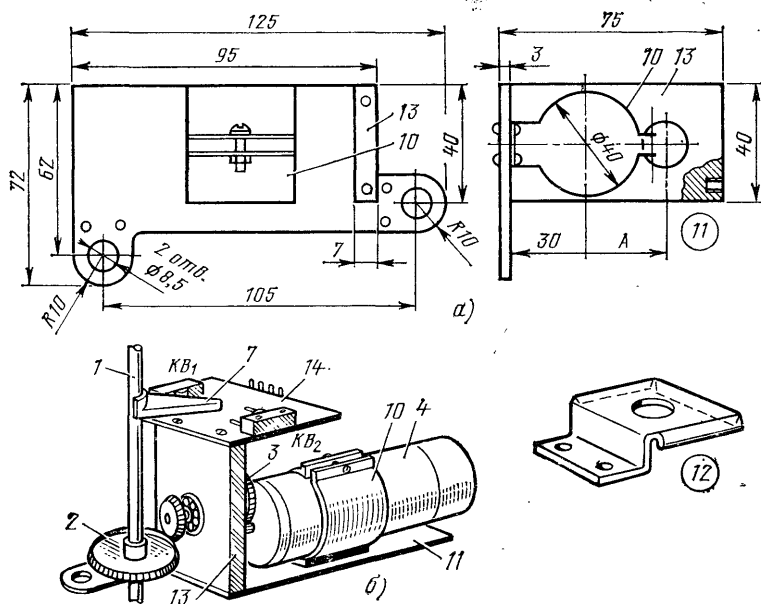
Детали крепления двигателя (а) и узел привода (б)
